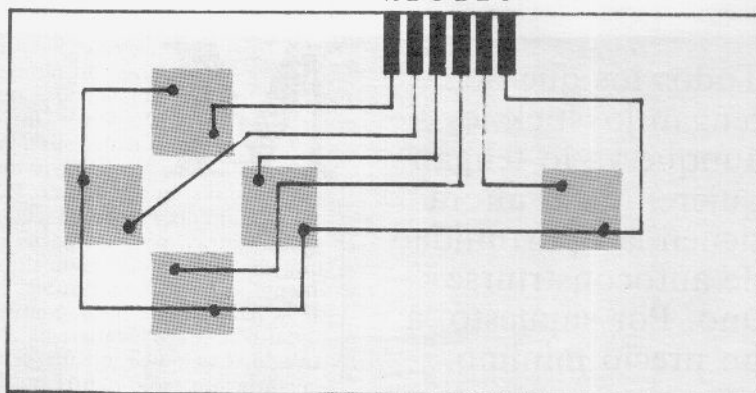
Placa para el joystick sin conector. Los cables han de ir soldados en los seis contactos que hay en la parte superior.
